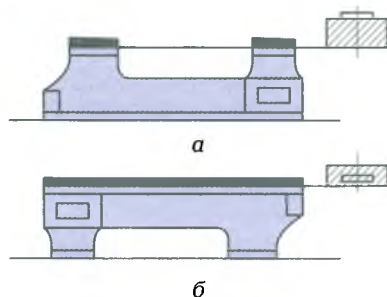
Схема последовательности обработки станины станка, обеспечивающая равномерность снимаемого слоя металла с направляющих:
